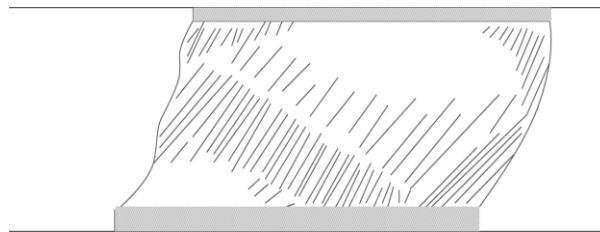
Mala auto-alineación de la unión de soldadura de un BGA [2].
